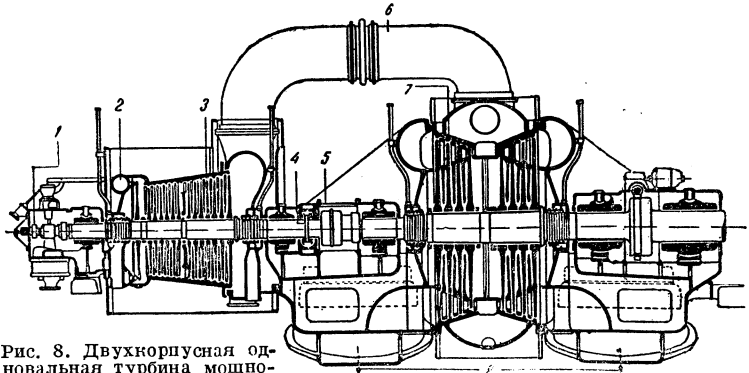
Двухкорпусная одновальная турбина мощностью 80 тыс. *квт*, с малым числом ступеней: 1—регулятор числа оборотов; 2—подвод свежего пара; 3—корпус высокого давления; 4—упорный подшипник; 5—муфта; 6—подвод пара в корпус низкого давления; 7—корпус низкого давления; 8—выпуск отработанного пара.
